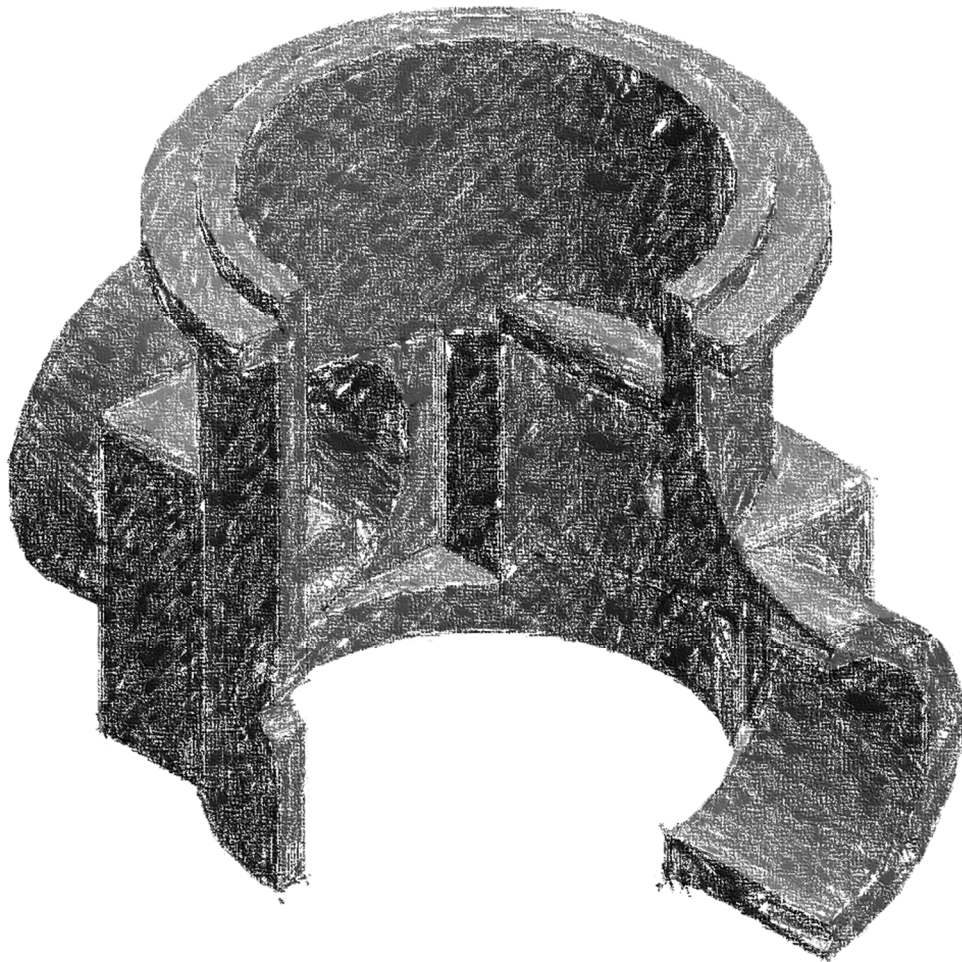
Корпус шкворневого пристрою в перерізі
